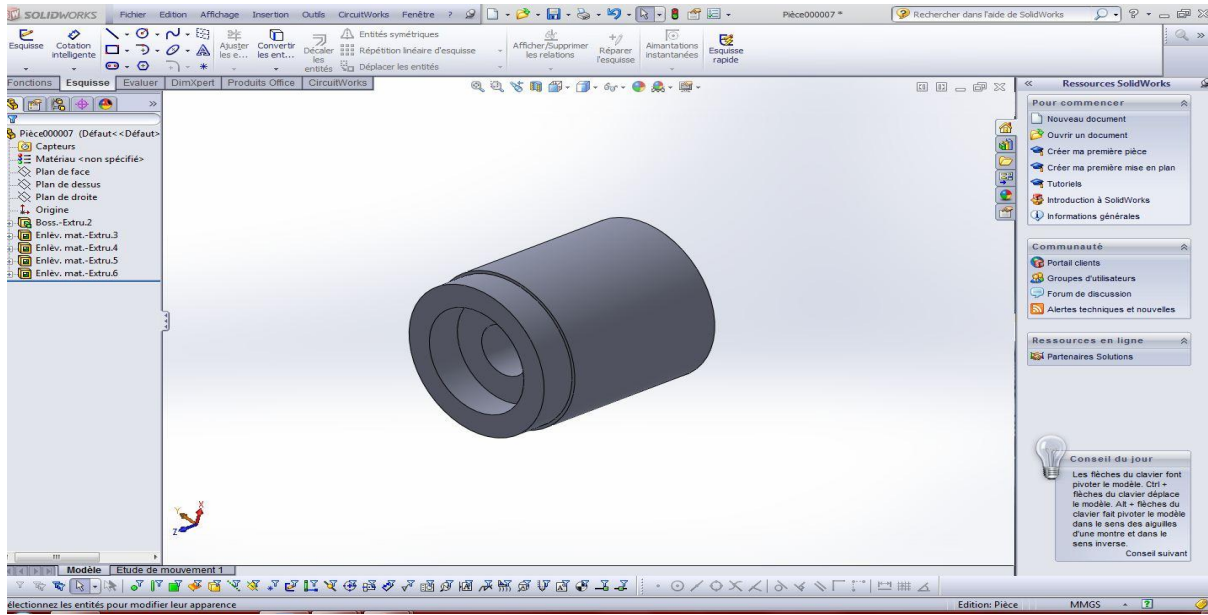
Vue Bague de fixation pour le Roulement réalisée sous SOLIDWORKS
